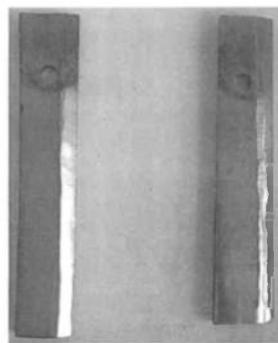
Образцы типоразмера №2 для стендовых испытаний на абразивное изнашивание
